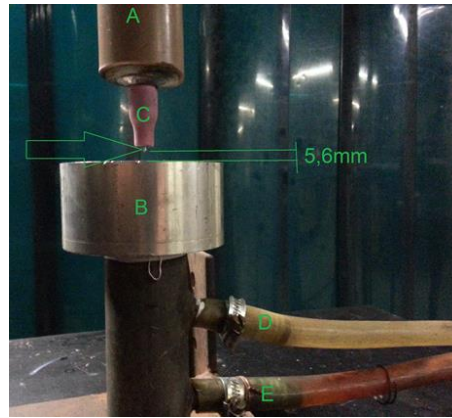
Detalhes da montagem. A - Tocha TIG. B - Bloco de alumínio. C - Bocal. D - Entrada (fria) de água de refrigeração do bloco. E - Saída (quente) de água de refrigeração do bloco. Seta: Eletrodo de tungstênio-comprimento do arco: 5,6mm
